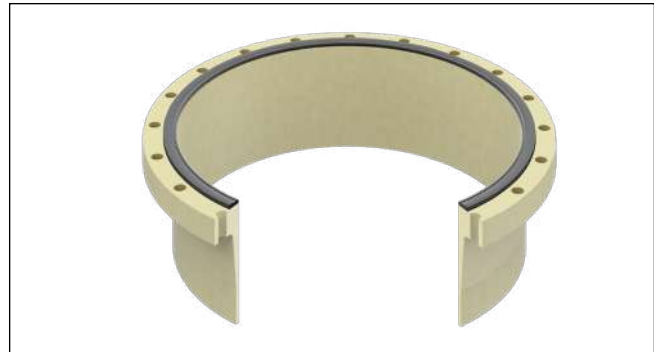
Junta flangeada perfil tipo anel (considerada na condição de face levantada para ajuste do binário)
